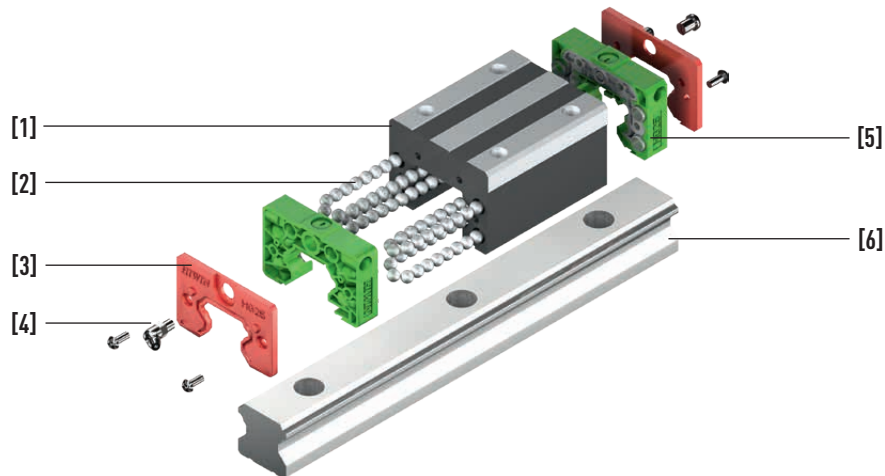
Explosionsdarstellung zum Aufbau einer Profilschienenführung
